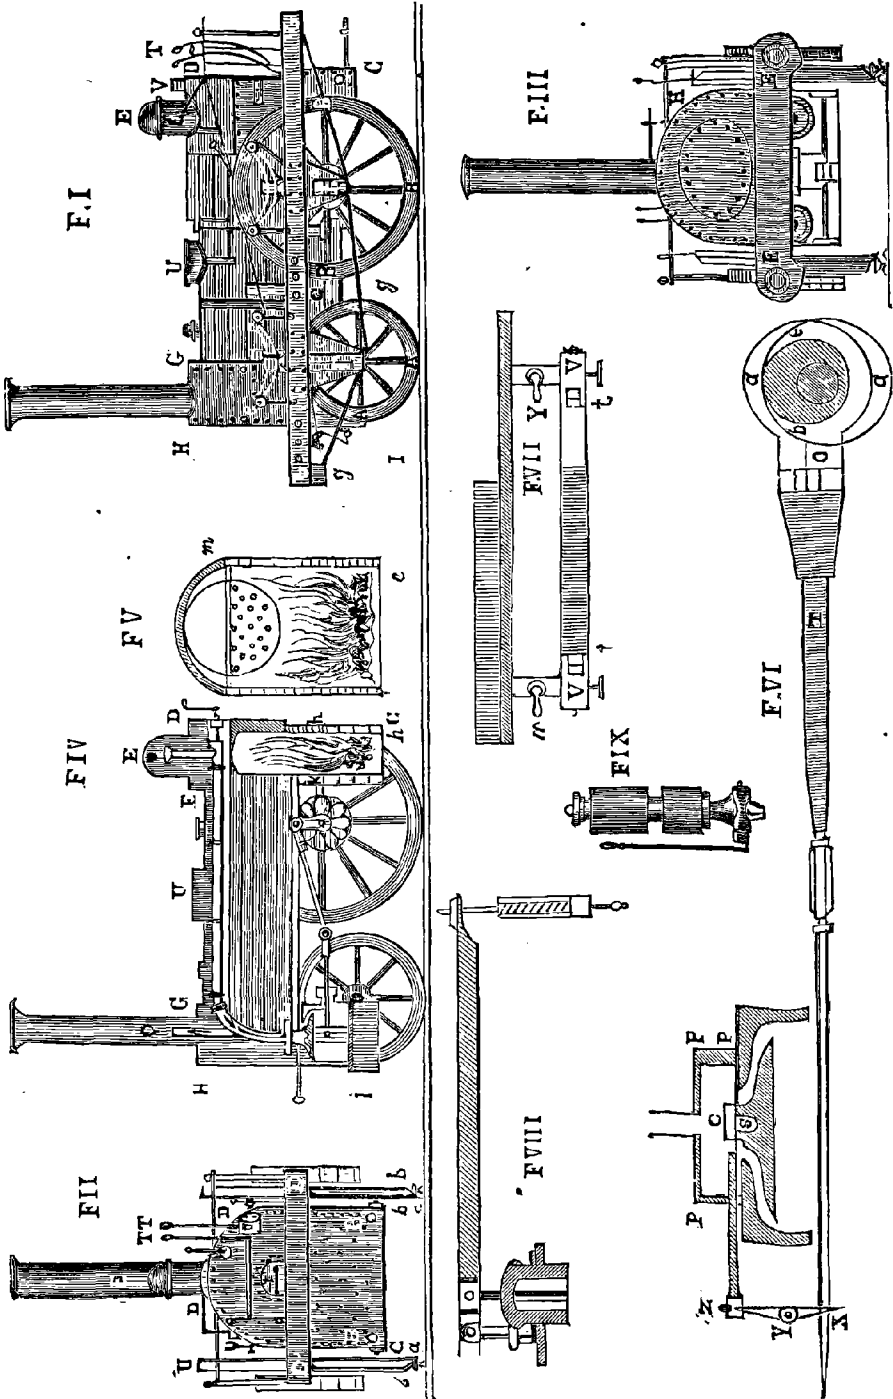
MACHINE HORIZONTALE LOCOMOBILE
